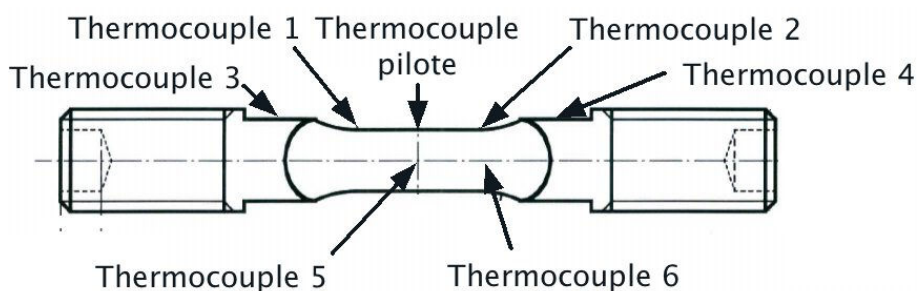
Emplacement des thermocouples pour l'éprouvette de géométrie rectangulaire
